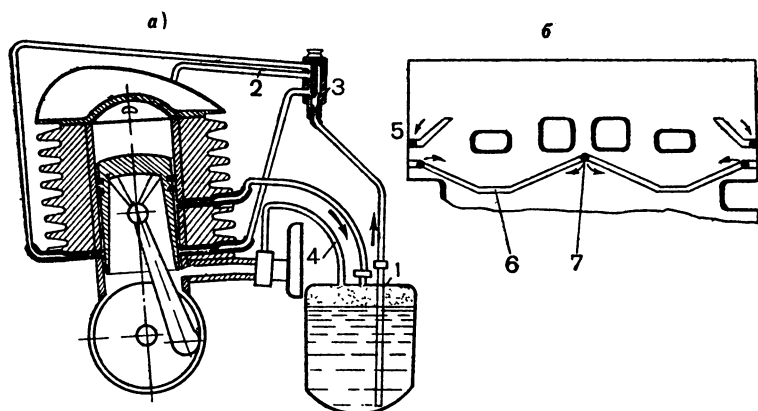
Схема системы смазки В. И. Кузьмина (а) и развертка цилиндра двигателя (б).
